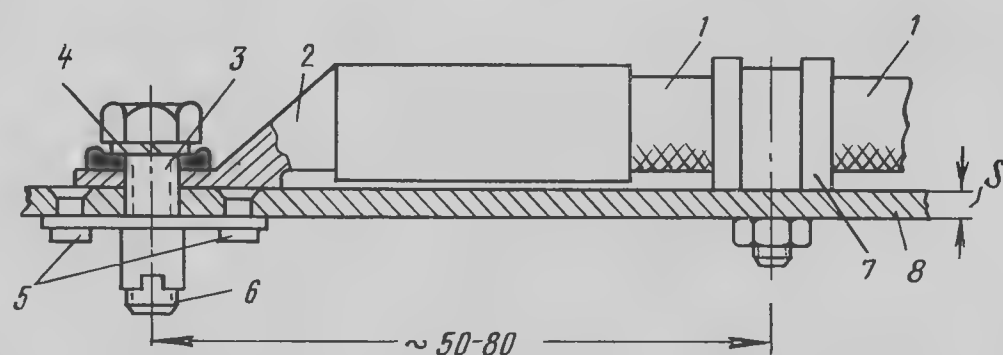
Присоединение минусового провода к корпусу объекта с помощью болта и самоконтрящейся гайки (3-й способ):
